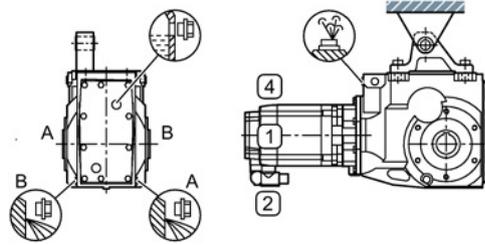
Einbautagen für Kegelradgetriebe K.F (Flansch-) und KAZ (Gehäuseflanschausführung), Baugröße 39 - 149, 3-stufig
